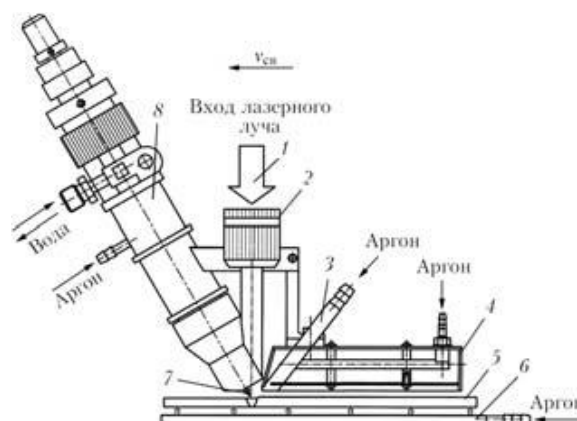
Схема гибридного лазерно-дугового процесса сварки:
